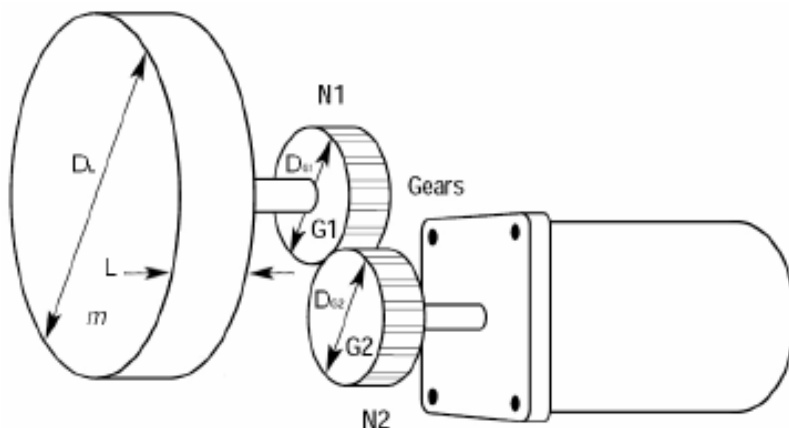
Representação da transmissão mecânica por relação de engrenagens
